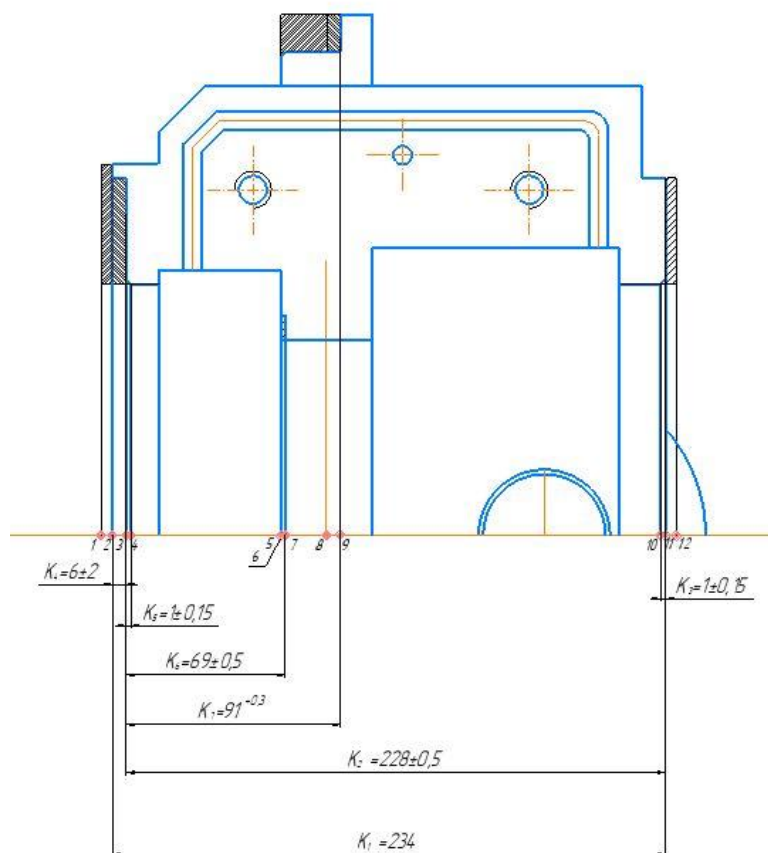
Эскиз детали «Корпус подшипника» с конструкторскими размерами
